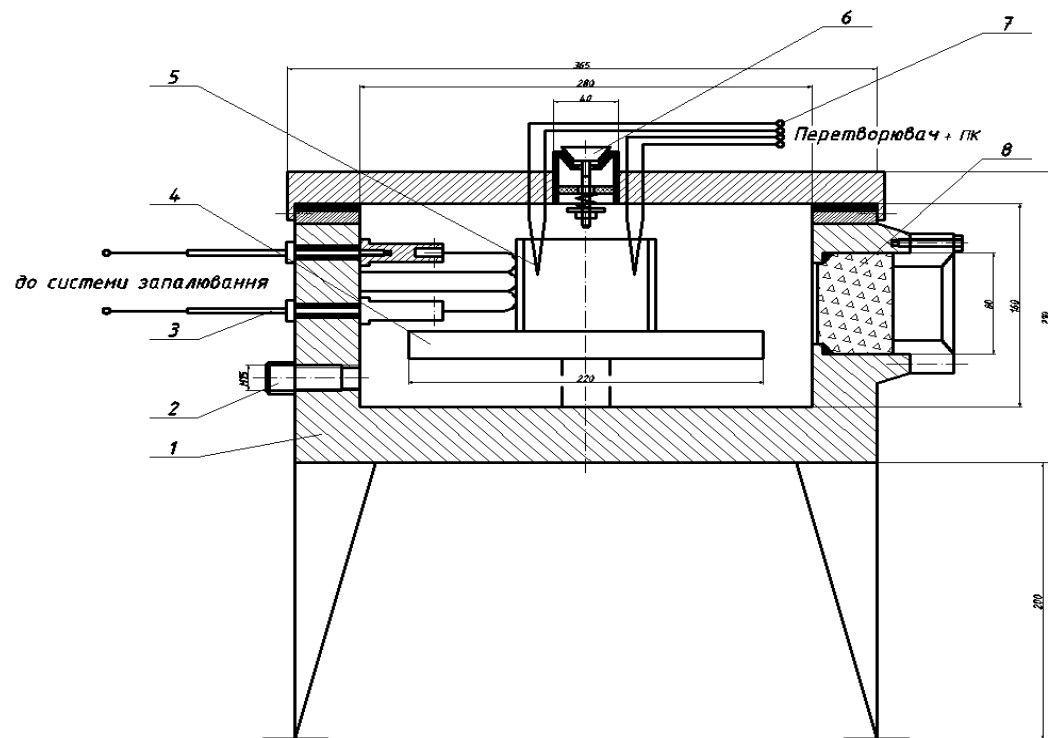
Реактор для реализации СВС процесса: 1 – корпус; 2 – штуцер; 3 – вольфрамовая спираль; 4 – предметный столик; 5 – контейнер с образцом; 6 – предохранительный клапан; 7 – термопары; 8 – окно наблюдения
